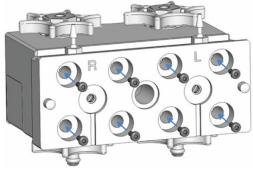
Pumpenkopf mit Hinterspülplatte und Schrauben für die Platte
